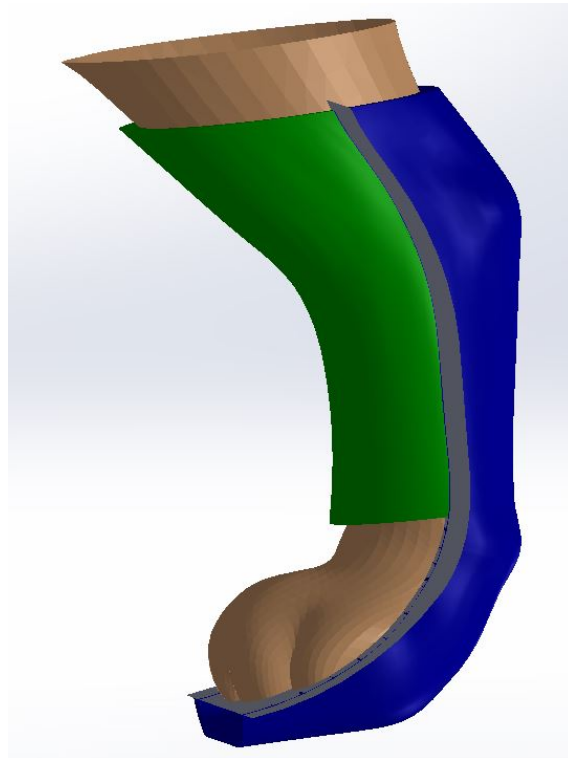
Sòlids inicials de la fèrula i superfície de tall
